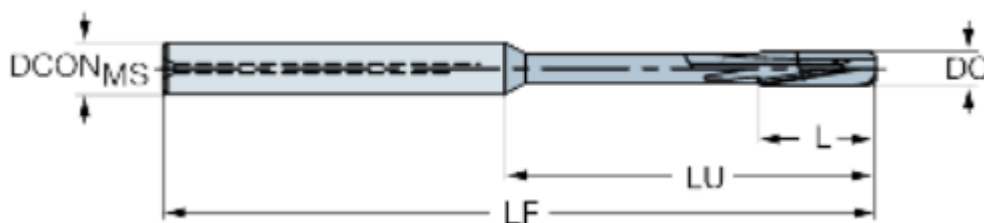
Розвіртка 835.T-1600-A1-PF 1024
